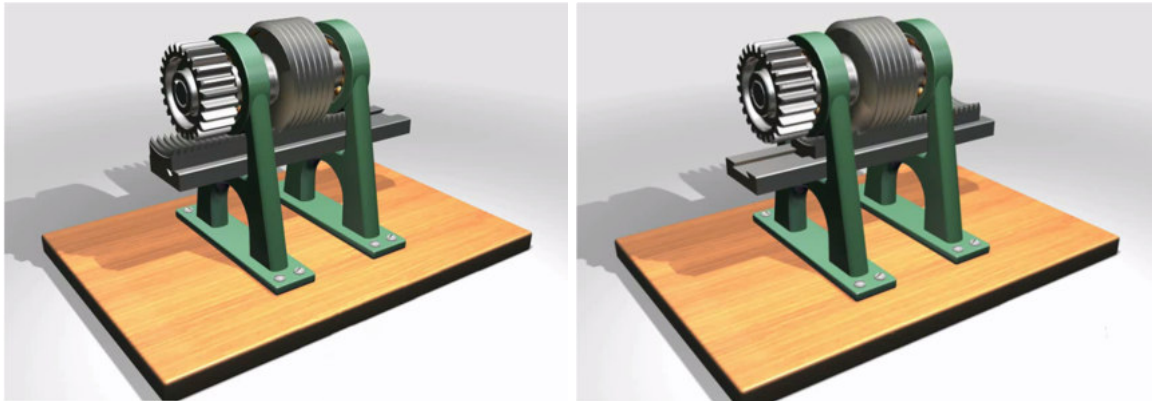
3D-модель черв'ячно-рейкової передачі (рейка рухома)
